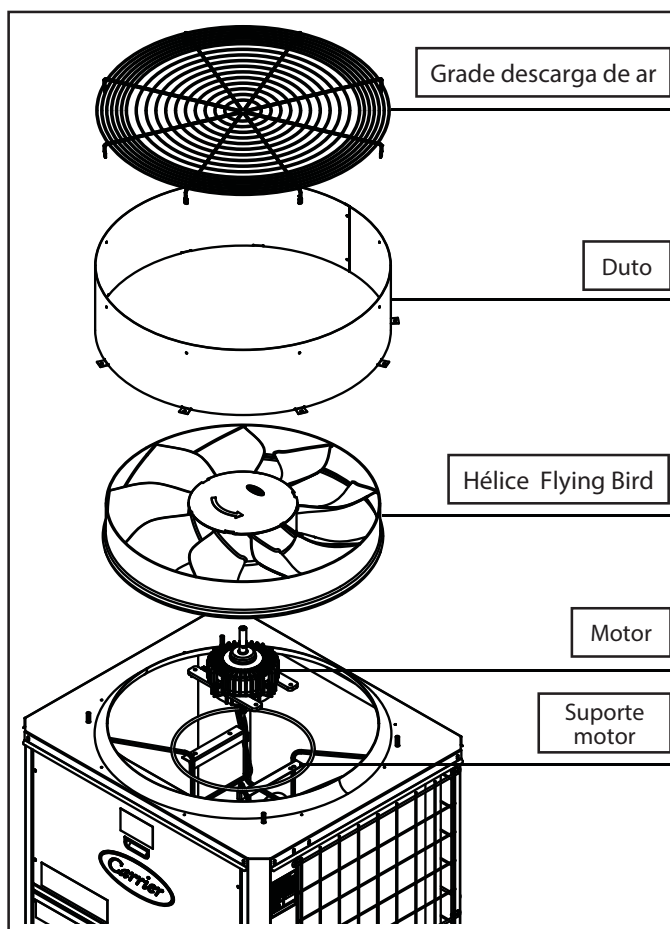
Vista explodida conjunto ventilador das unidades 30EX/30EV e Hélice Flying Bird
